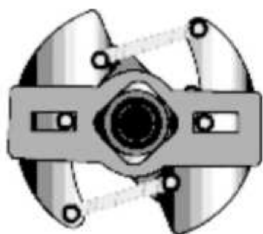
Схема расположения деталей центробежного регулятора угла опережения зажигания: 1 – кулачок прерывателя; 2 – втулка кулачков; 3 – подвижная пластина; 4 – грузики; 5 – шипы грузиков; 6 – опорная пластина; 7 – приводной валик; 8 – стяжные пружины.
